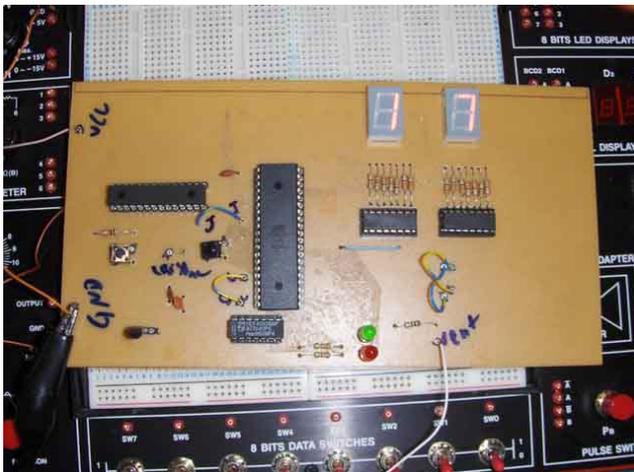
Placa do circuito controlador da temperatura – Face dos componentes
